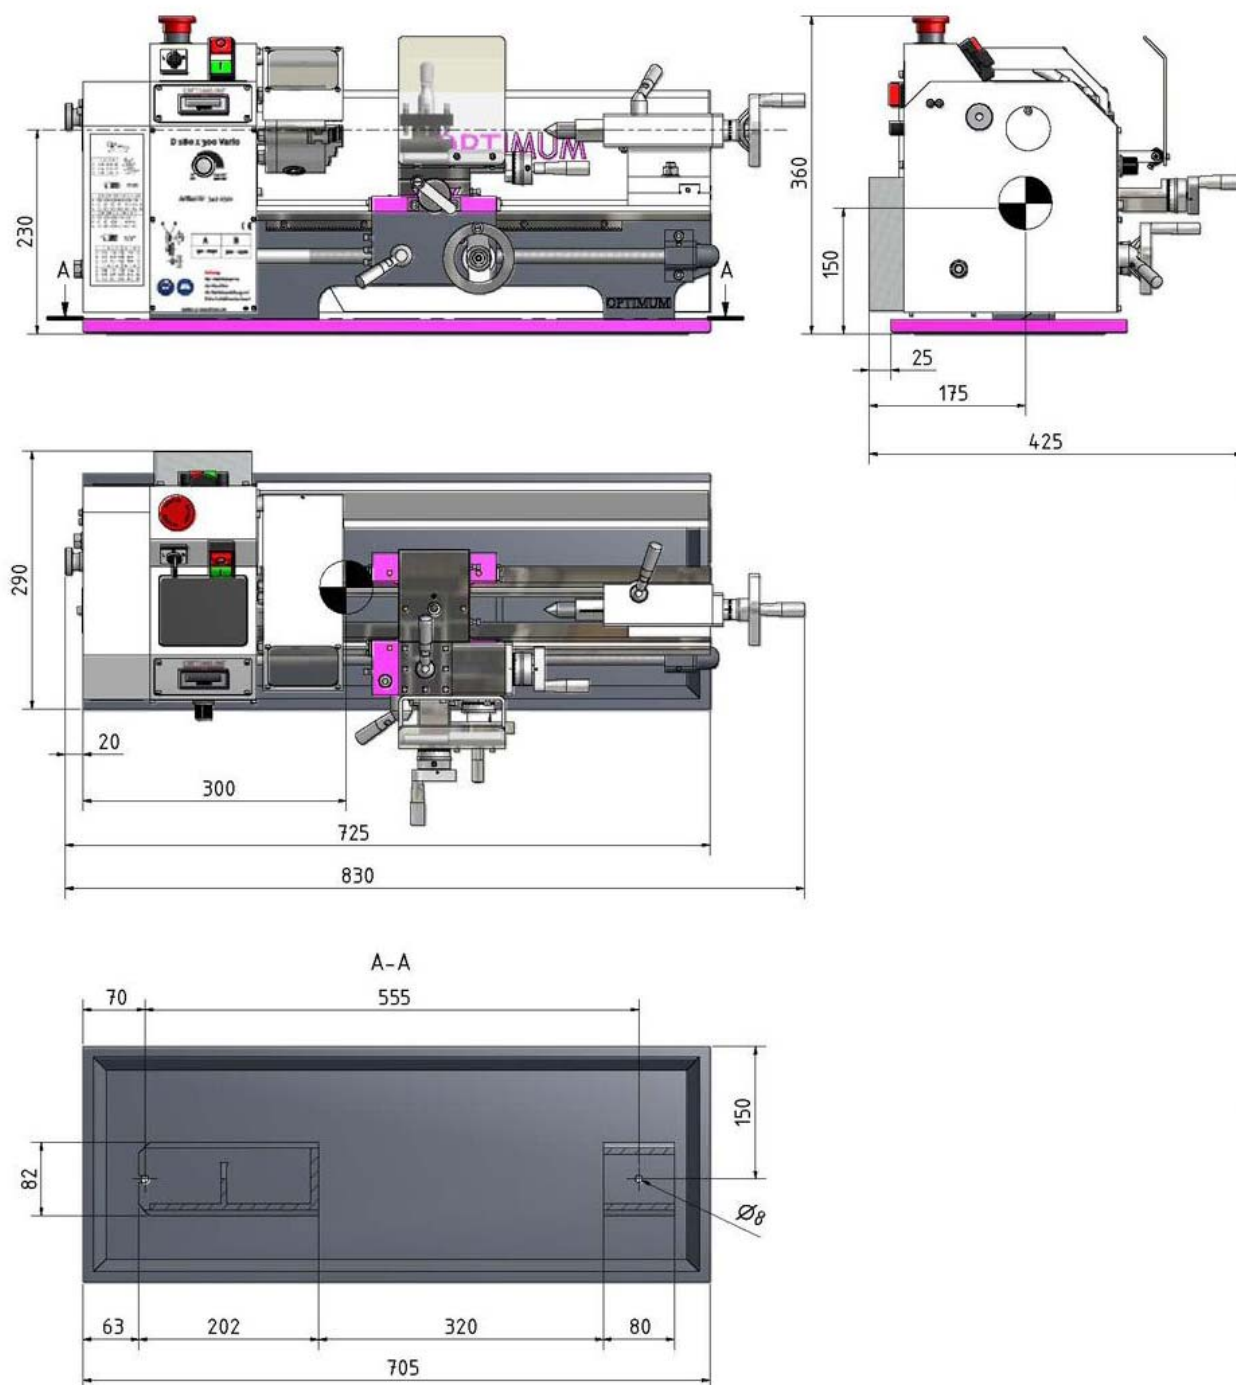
Dimensiones, plano de instalación - D180x300 Vario
